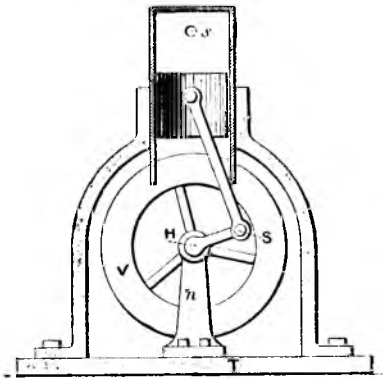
Основные части всякого двигателя с возвратно движущимися частями. — s , пространство цилиндра над поршнем. — S , кривошип, или цапфа — шейка колена вала. — H , центр главного вала (коленчатого). — V , маховик. — $л$, основание (стойка) для подшипников (коренных) главного вала. — T , фундамент-плита (основание).
